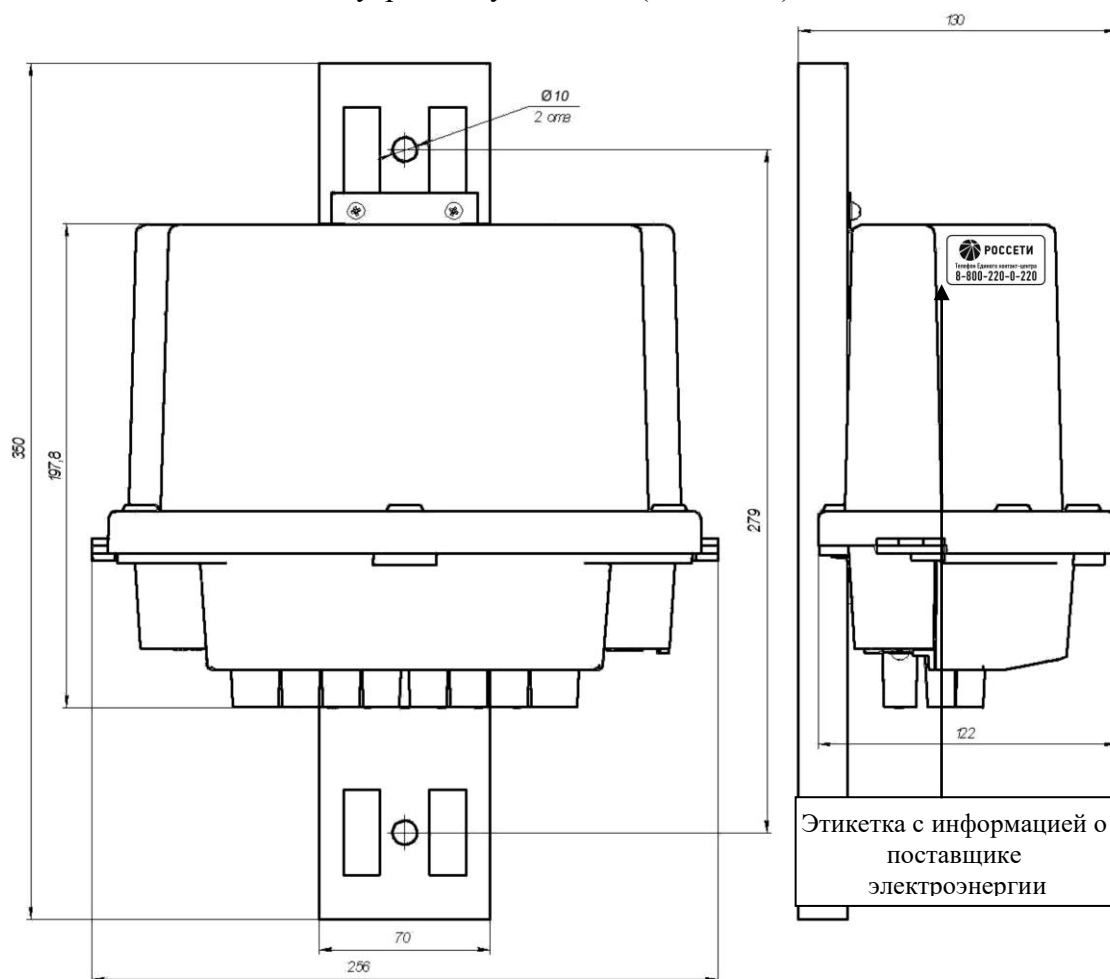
Габаритный чертеж и установочные размеры счётчика наружной установки
